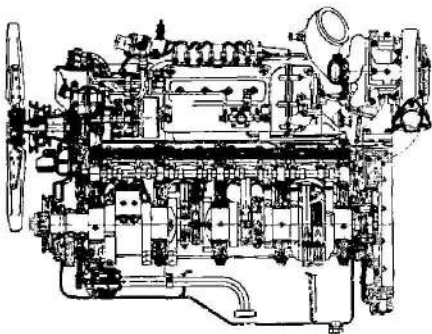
а. Продольный разрез двигателя ЯМЗ – 238 НД
